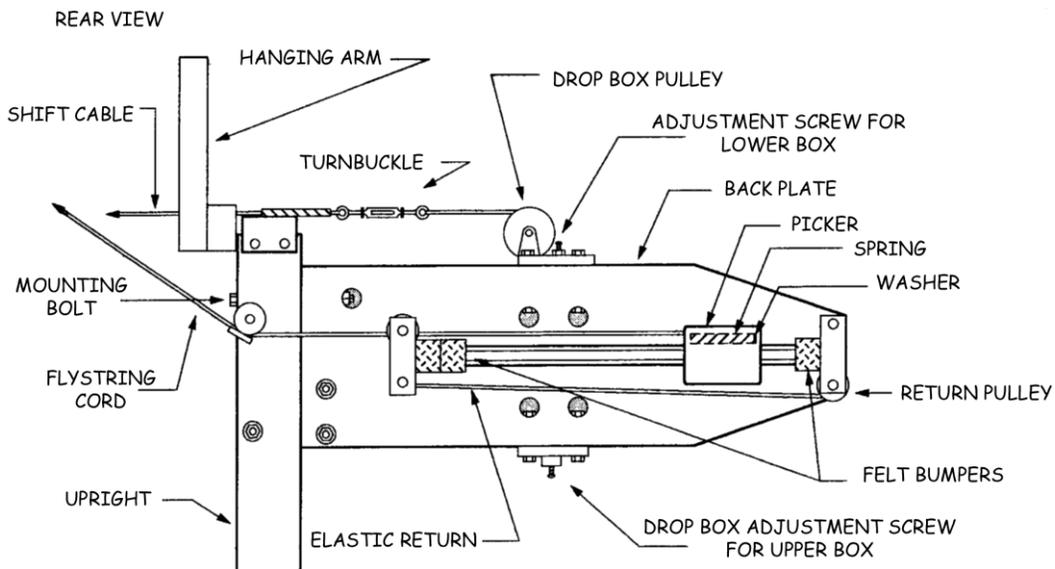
Assemblage de la boîte de dépôt par l'arrière
